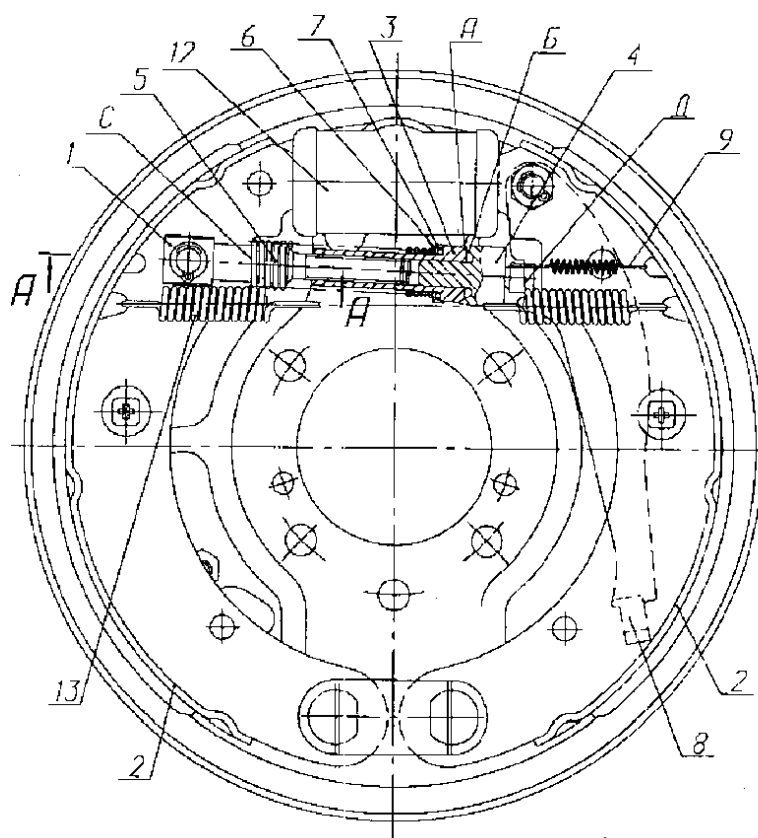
Устройство автоматической регулировки зазора барабанного тормоза и привода стояночного тормоза. Патент Германии № DE 10121968
